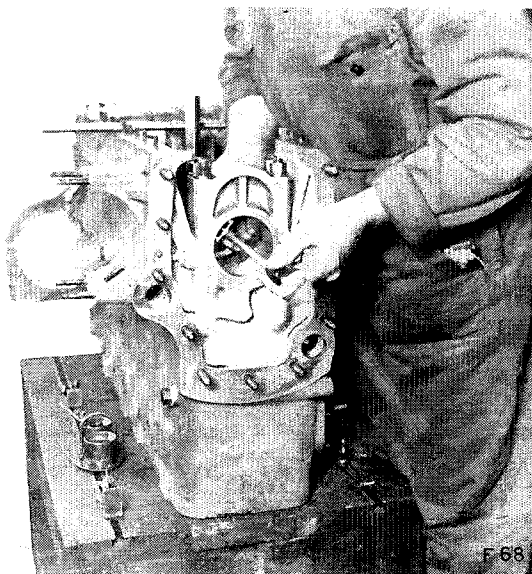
Nachmessen der Hauptlagerbohrungen mit eingebauten Lagerschalen
